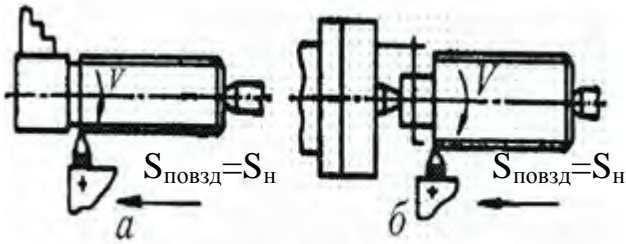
Схеми нарізування однозахідної (а) і багатозахідної (б) різьб на токарно-гвинторізному верстаті
